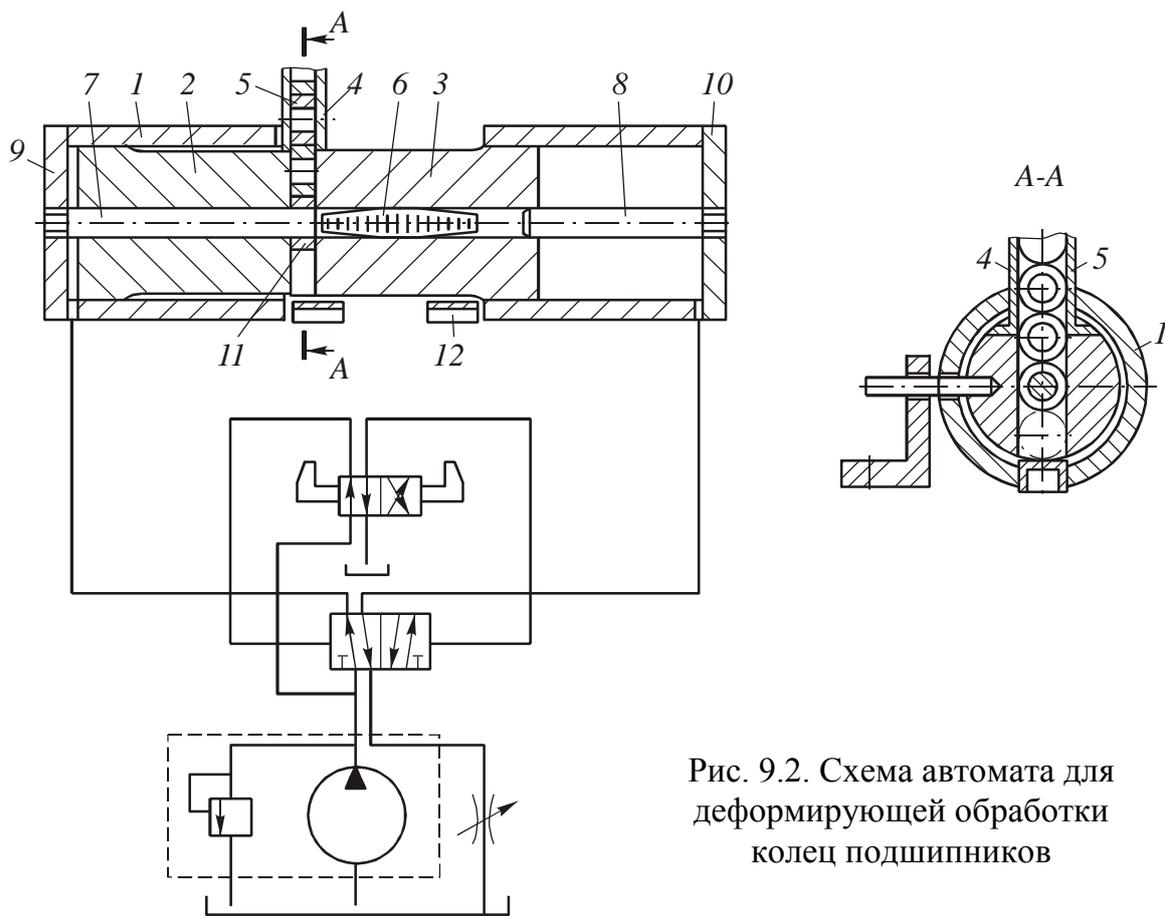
Схема автомата для деформирующей обработки колец подшипников
